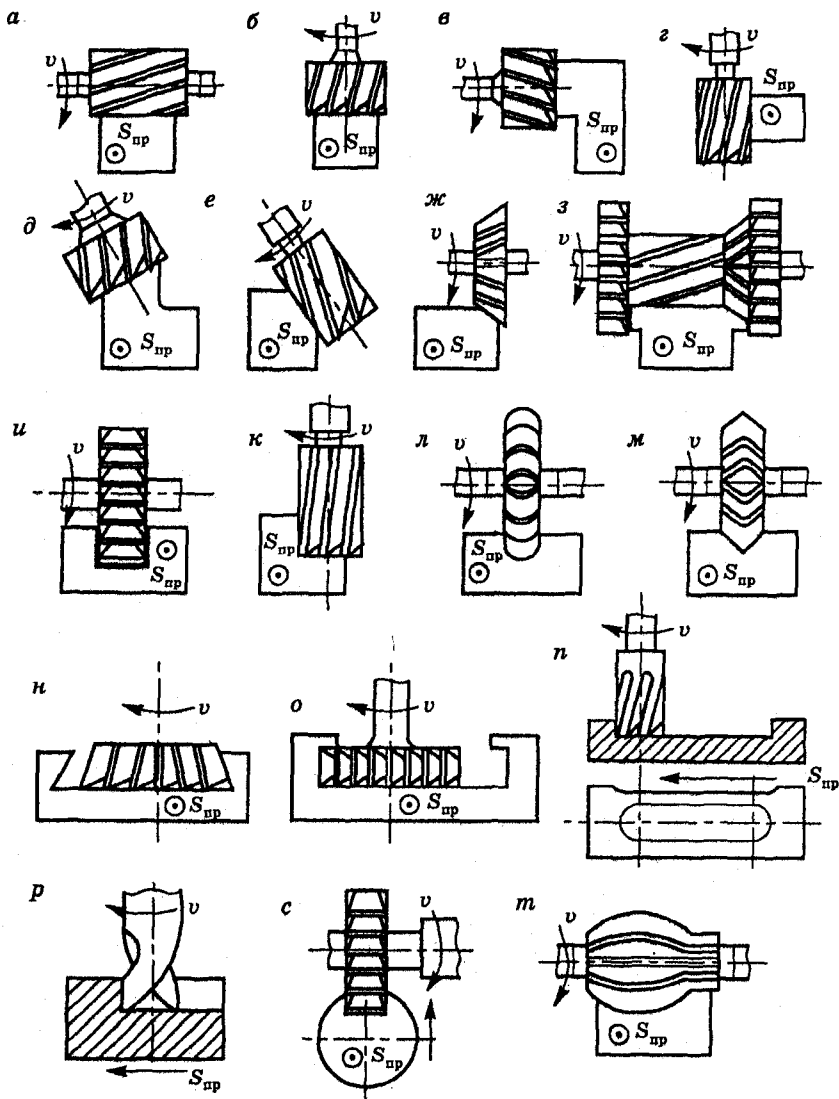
Виды фрез и схемы обработки фрезерованием
